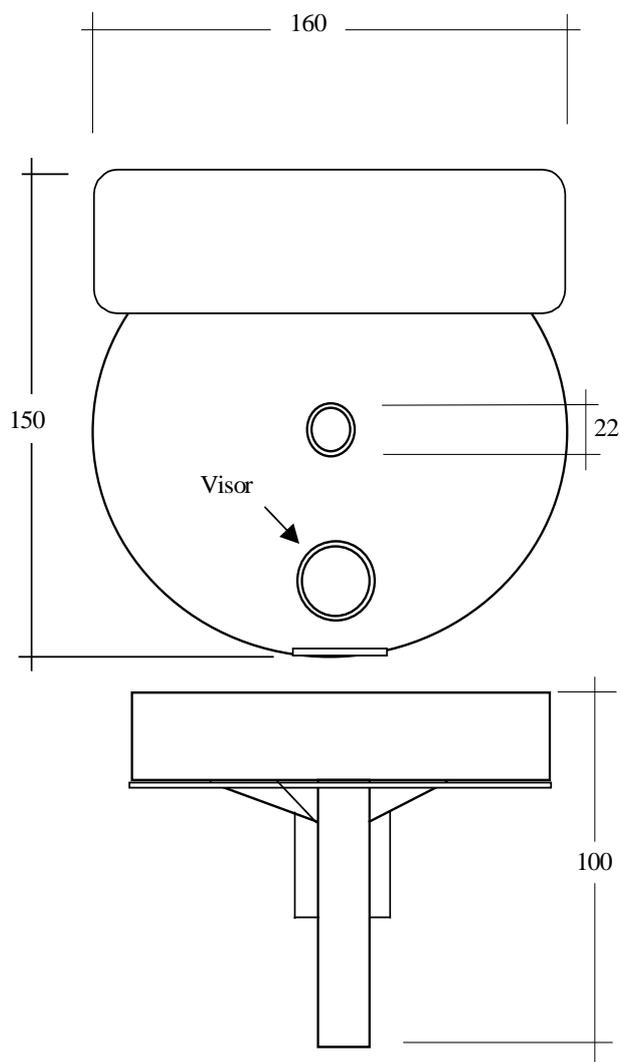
Geometria (sem escala) e dimensões (em mm) gerais do interruptor anti-furto.
